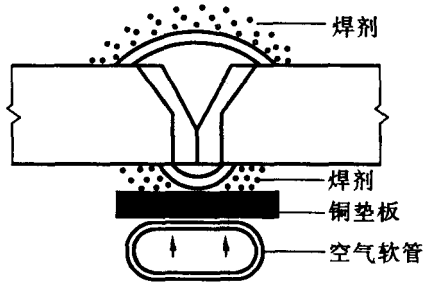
焊剂铜衬垫法 (FCB 法)
